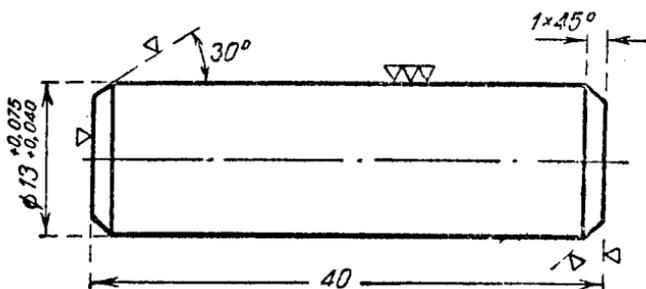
Дет. 12-06. Палец внутренней ведомой шестерни
